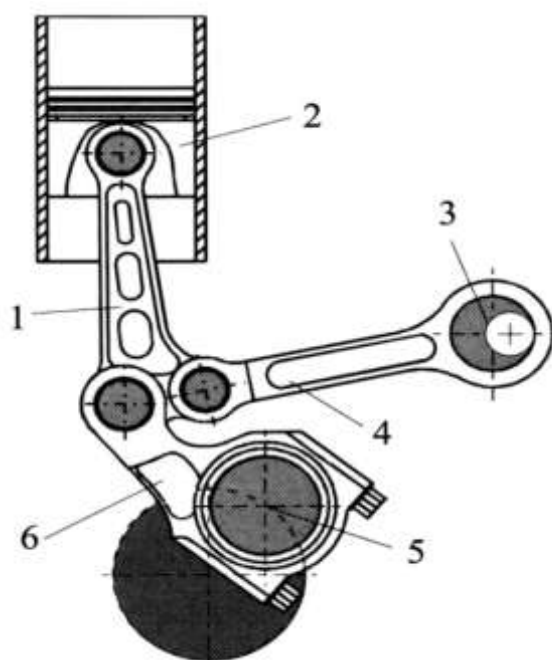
Схема двигателя с изменяемой степенью сжатия с дополнительным шатуном: 1 - шатун; 2 - поршень; 3 - эксцентриковый вал; 4 - дополнительный шатун; 5 - шатунная шейка коленчатого вала; 6 - коромысло
